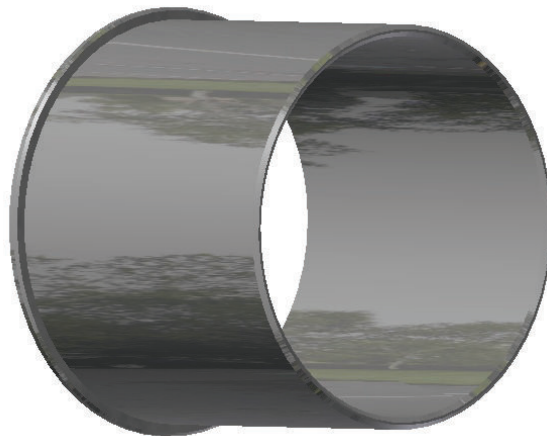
Cojinetes de deslizamiento hidráulicos
